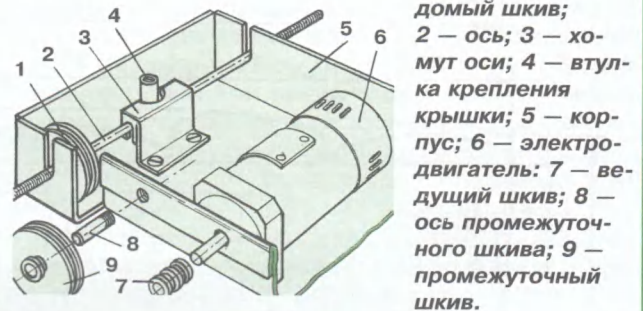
Конструкция механического блока: 1 — ведомый шкив; 2 — ось; 3 — хомут оси; 4 — втулка крепления крышки; 5 — корпус; 6 — электродвигатель; 7 — ведущий шкив; 8 — ось промежуточного шкива; 9 — промежуточный шкив.
